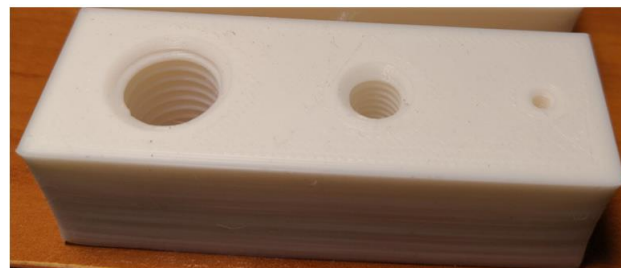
Образец с внутренними резьбами напечатанный на 3D-принтере MakerBot Method X
